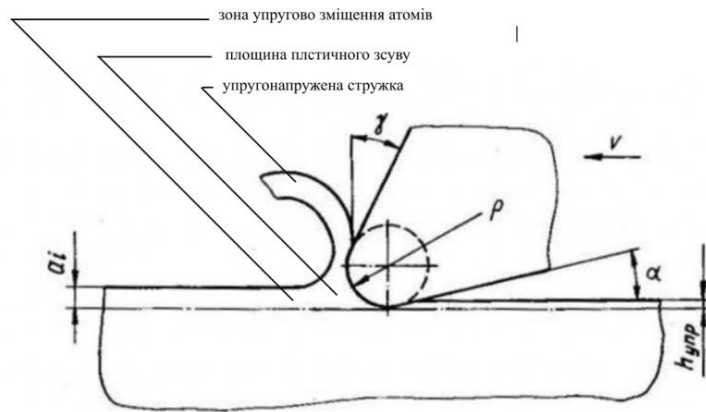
Схема врізання зуба фрези при швидкісному зубофрезеруванні
